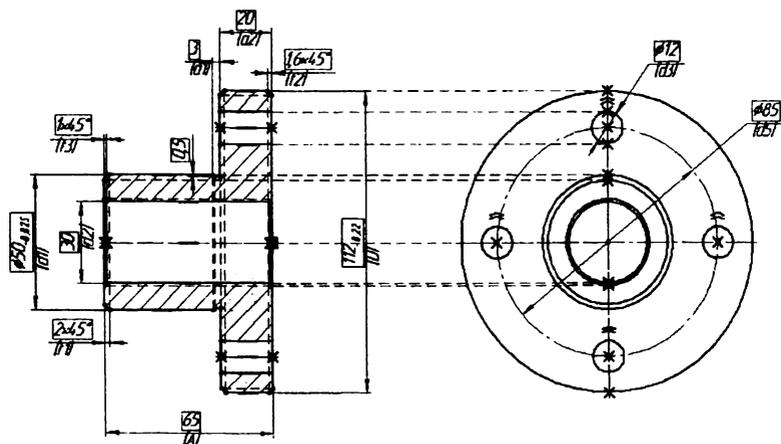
Главный вид и сечение детали Фланец с привязками (вариант)
